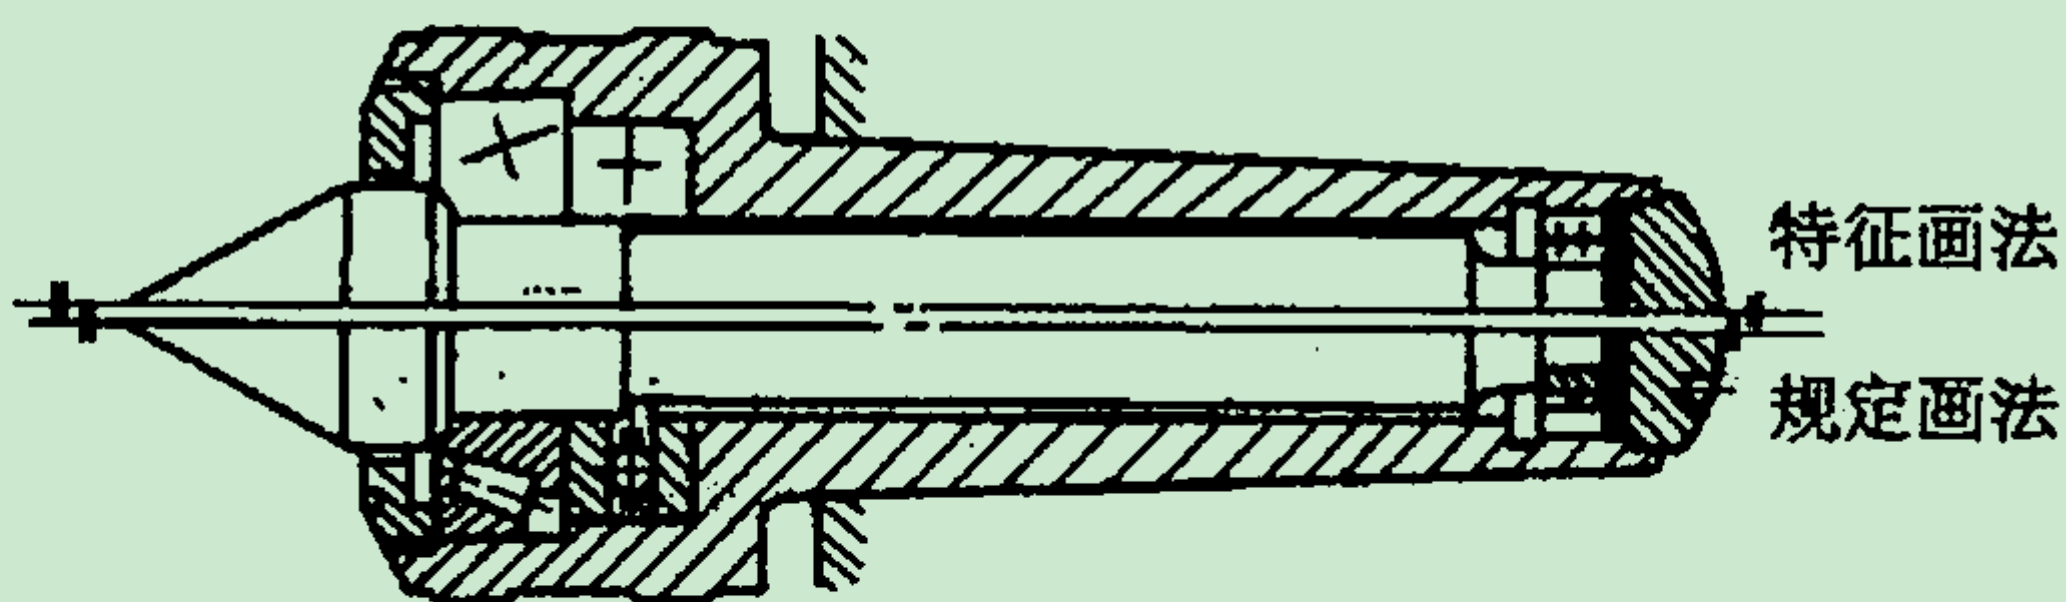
圆锥滚子轴承、推力球轴承和双列深沟球轴承在装配图中的画法
